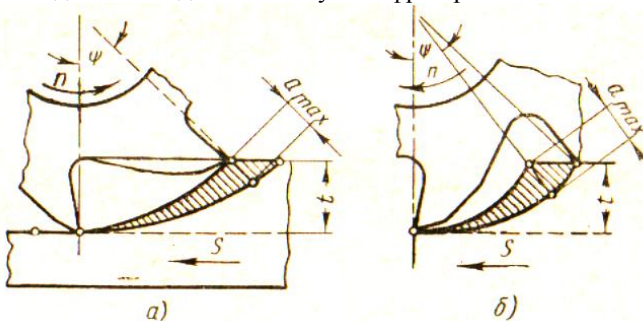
Схемы фрезерования: а- встречное; б – попутное.
